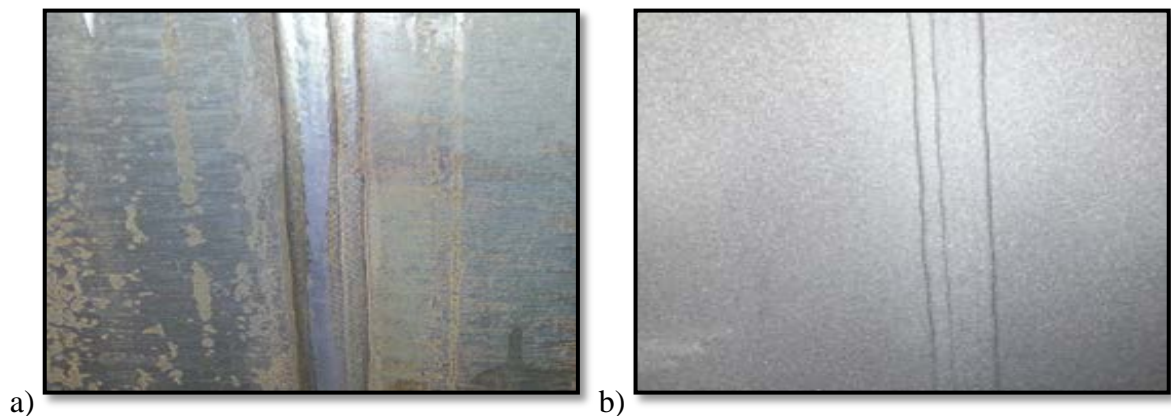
Zona de soldadura de um troço: a) Antes do processo de decapagem;
